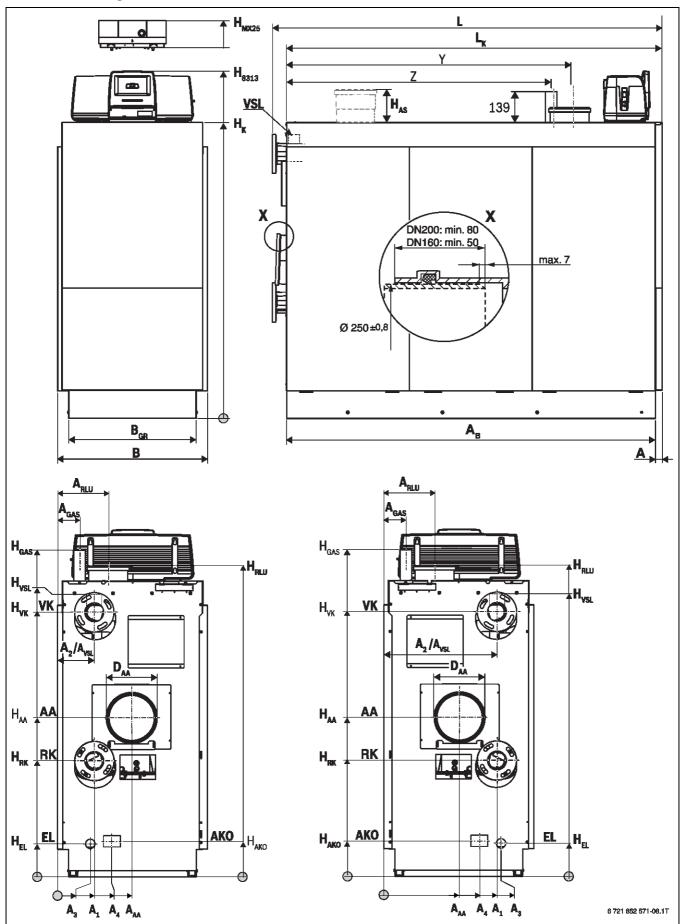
Abmessungen und Anschlüsse Condens 7000 FP, 350 ... 500 kW (rechte und linke Ausführung: Maße in mm)
